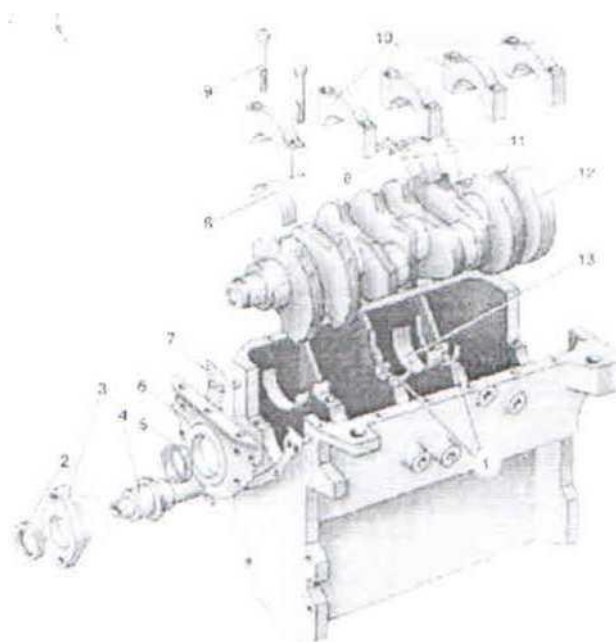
Коленчатый вал и блок цилиндров
